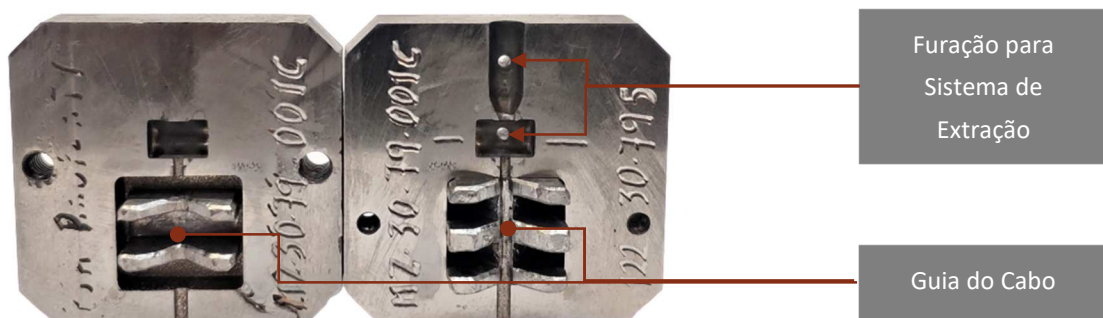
Exemplo de molde para terminal de injeção de Zamak
